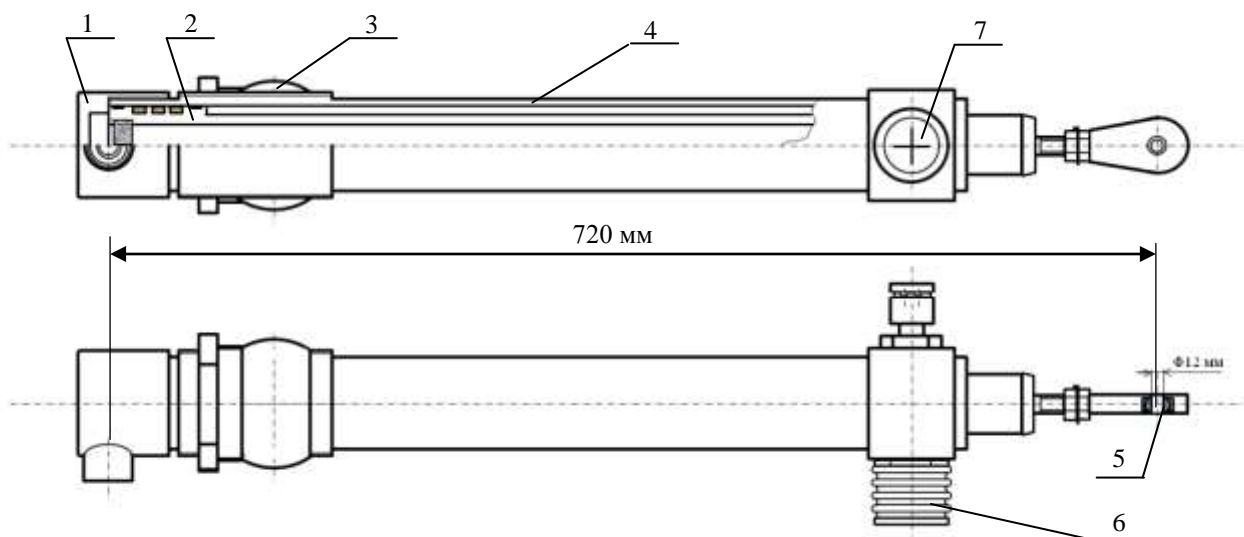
Привод газогидравлический (внутренняя полость гидравлическая, слив при выдвигании штока через дроссельную шайбу) с ходом штока 500 мм. На рис.: 1 – корпус подвода газового давления; 2 – шток; 3 – шарнирная опора; 4 – цилиндр; 5 – сферический подшипник серьги крепления штока; 6 – сильфонный термокомпенсатор; 7 – прорывная мембрана.
